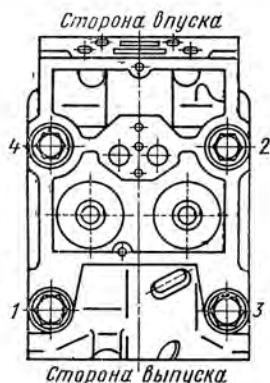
Порядок затяжки болтов крепления головки цилиндра
